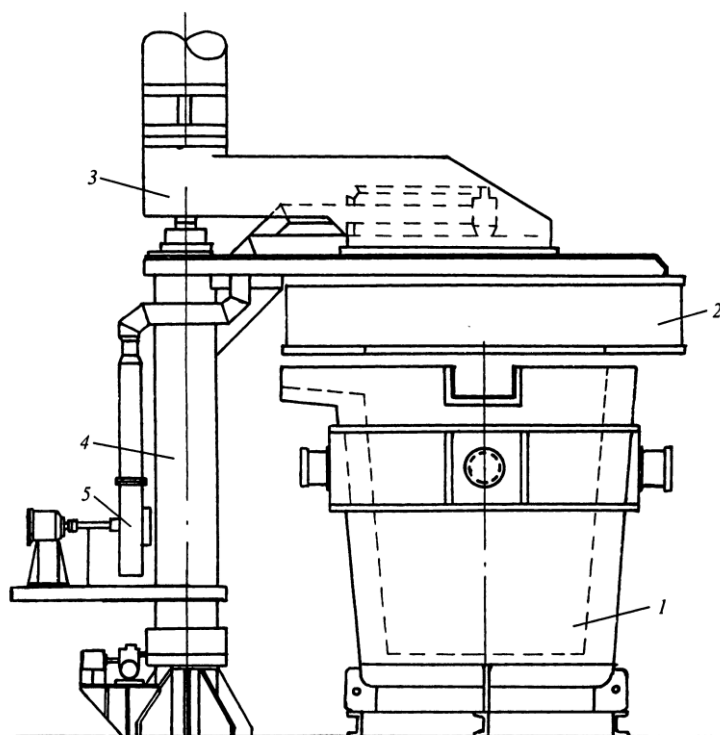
Стенд сушки футеровки с поворотной крышкой: 1 – ковш; 2 – крышка с горелкой; 3 – дымоотводящий тракт; 4 – поворотная стойка; 5 – вентилятор
